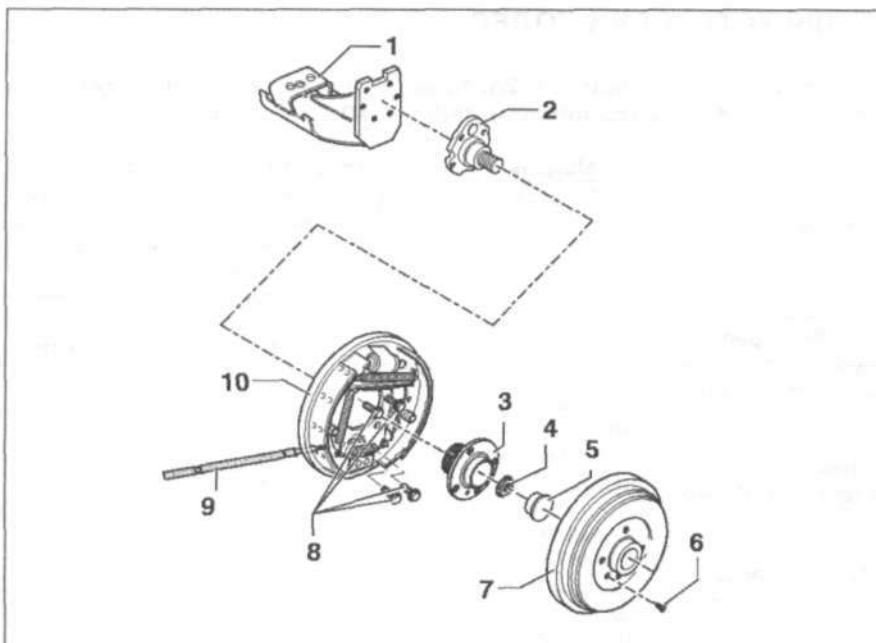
Колесный подшипник автомобиля Caddy с 10.99 г. выпуска:
